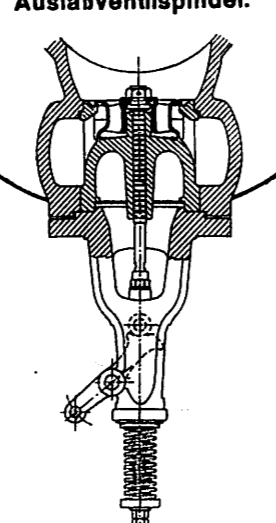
bis 14. Lentz-Dichtung für Dampfmaschinen.
